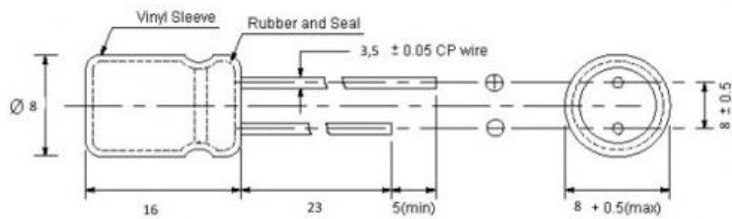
Габаритні розміри конденсатора типу ЕСАР
